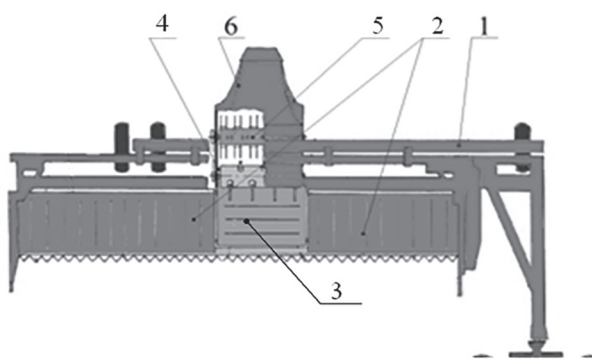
Прицепной жатвенный агрегат на базе прицепной валковой жатки для измельчения очесанного стеблестоя, его разбрасывания по полю, или погрузки в транспортное средство:
